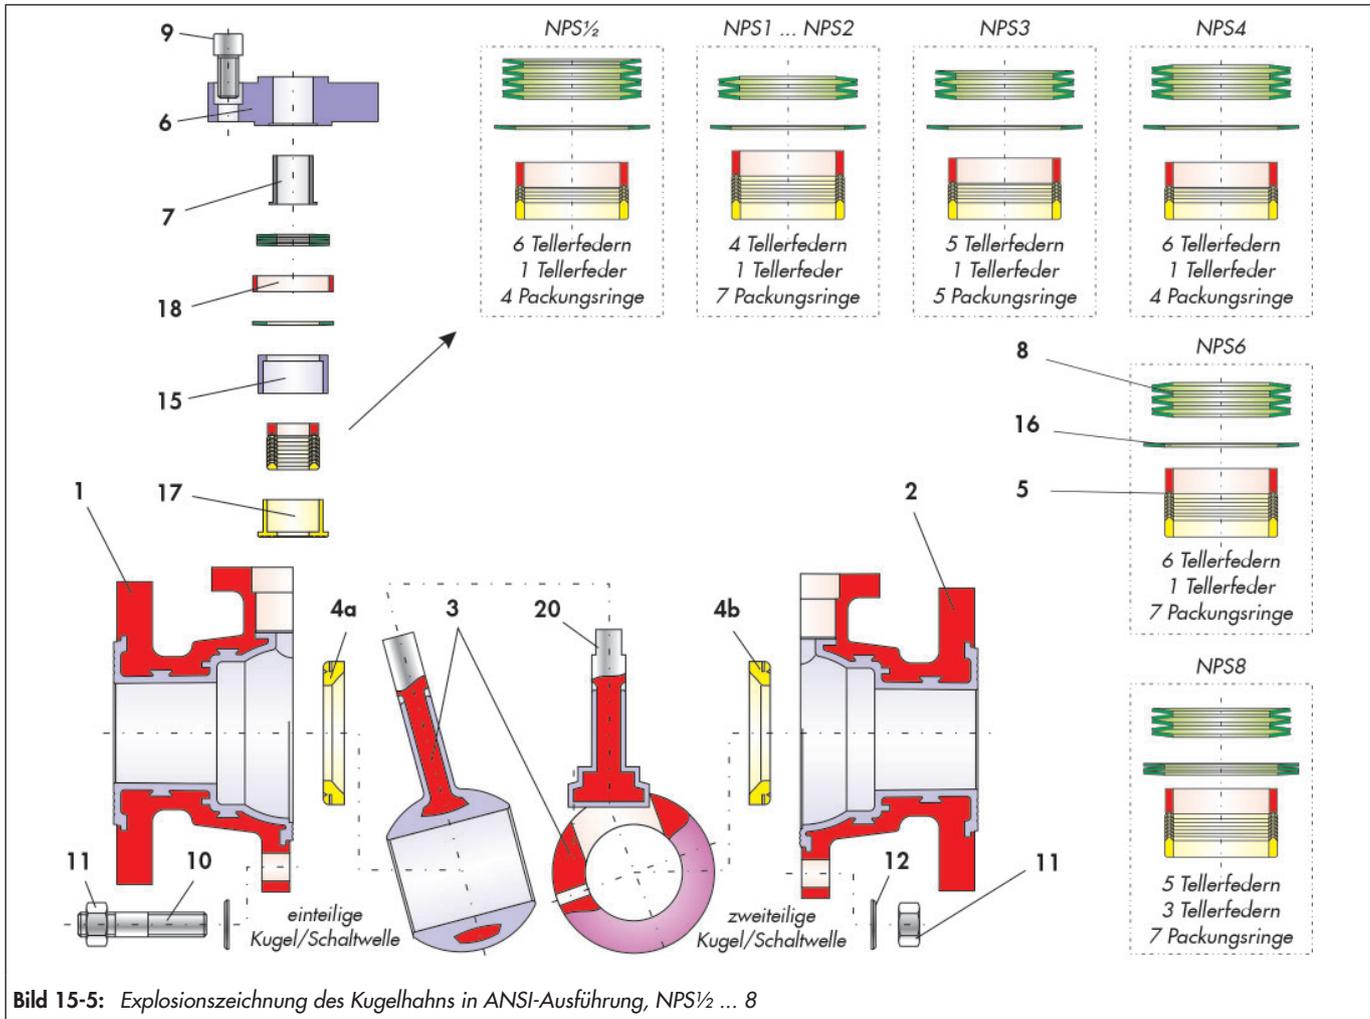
Explosionszeichnung des Kugelhahns in ANSI-Ausführung, NPS½ ... 8
